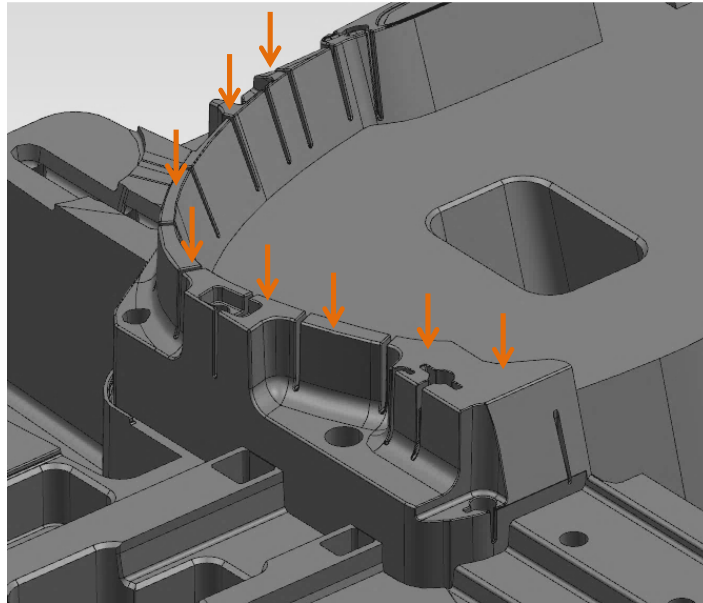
Zona moldante do molde de fabrico convencional, *Blende
